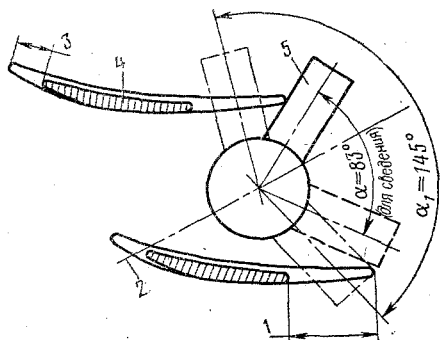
Схема расположения ножки прибора ПМ-2 при замере износа лопатки НА шестой ступени компрессора:
